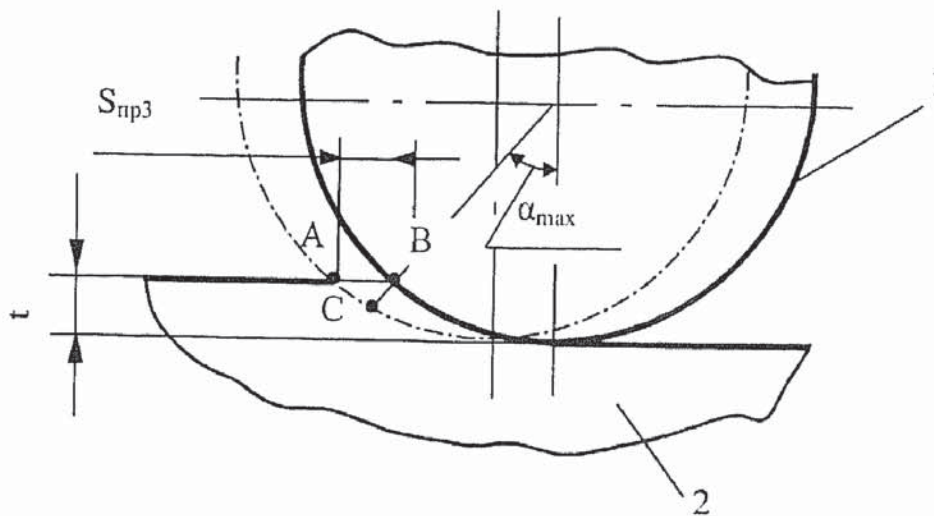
Схема к расчету глубины внедрения АЗ в заготовку: 1 — ШК; 2 — заготовка
